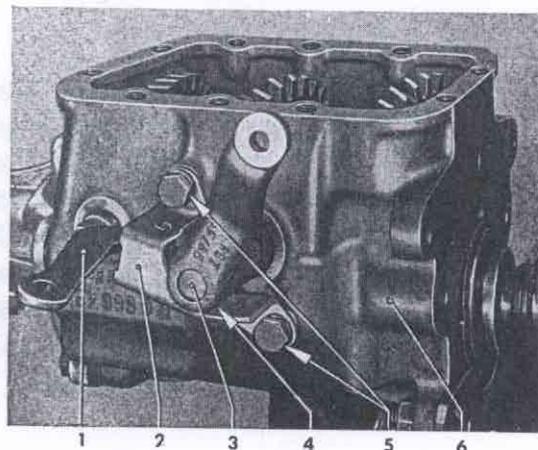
Befestigung Lagerbock für Umschalthebel am Getriebegehäuse
